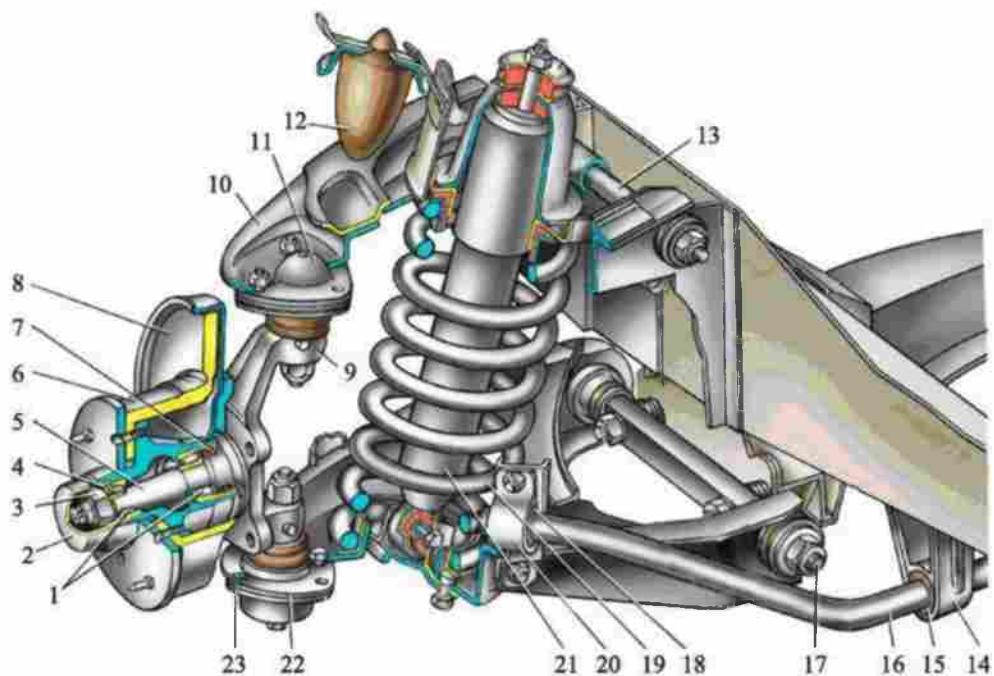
Детали передней подвески: 1 - подшипники ступицы переднего колеса; 2 - колпак ступицы; 3 - регулировочная гайка; 4 - шайба; 5 - цапфа поворотного пальца; 6 - ступица колеса; 7 - сальник; 8 - тормозной диск; 9 - поворотный кулак; 10 - верхний рычаг подвески; 11 - корпус подшипника верхней опоры; 12 - буфер хода сжатия; 13 - ось верхнего рычага подвески; 14 - кронштейн крепления штанги стабилизатора; 15 - подушка штанги стабилизатора; 16 - штанга стабилизатора; 17 - ось нижнего рычага; 18 - подушка штанги стабилизатора; 19 - пружина подвески; 20 - обойма крепления штанги амортизатора; 21 - амортизатор; 22 - корпус подшипника нижней опоры; 23 - нижний рычаг подвески На повороте кузов автомобиля одним своим боком прижимается к земле, в то время как второй бок хочет уйти в отрыв от земли. В отрыв ему не дает возможности уйти стабилизатор, который, прижавшись к земле одним концом, вторым своим концом прижимает и другую сторону автомобиля. При наезде какого-либо колеса на препятствие стержень стабилизатора закручивается и стремится побыстрее вернуть это колесо на свое место.
